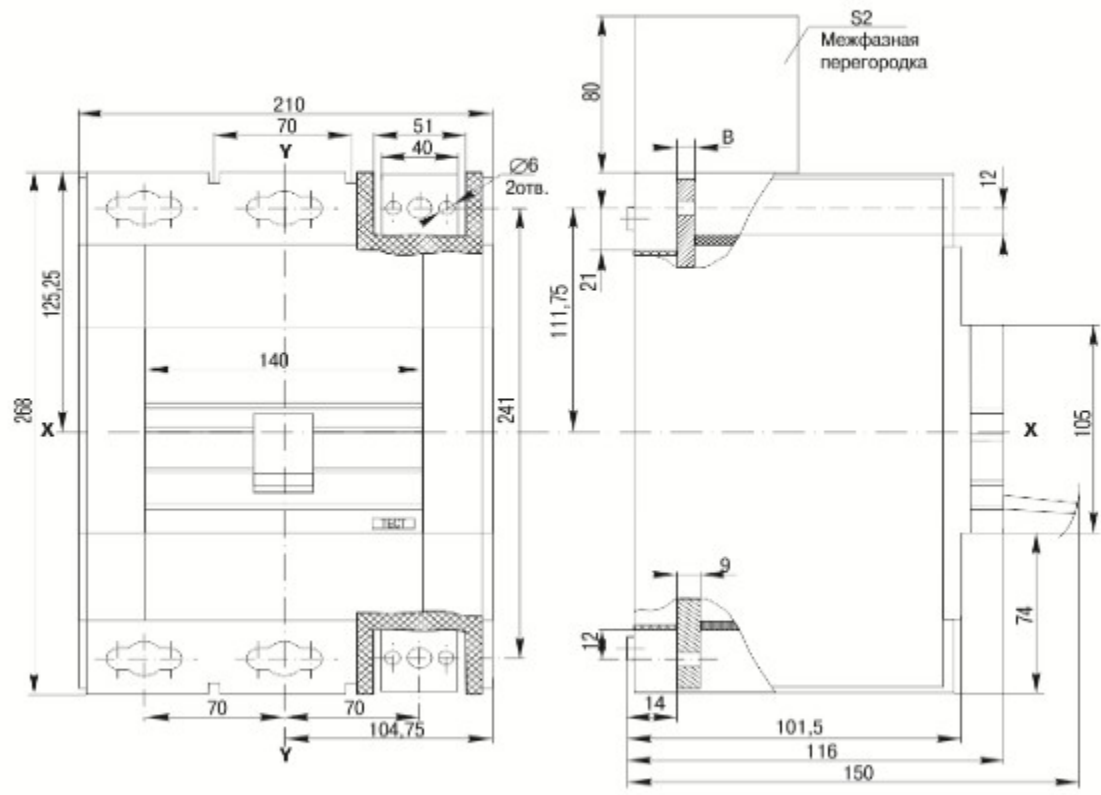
Габаритные и установочные размеры выключателя BA88-35
